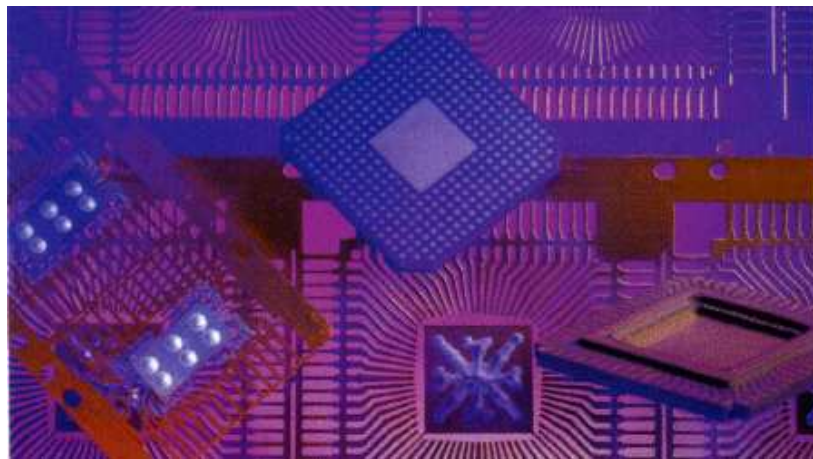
Fabrication de composants électroniques: moulage, découpage des pattes, formation des pattes, inspection des billes.
